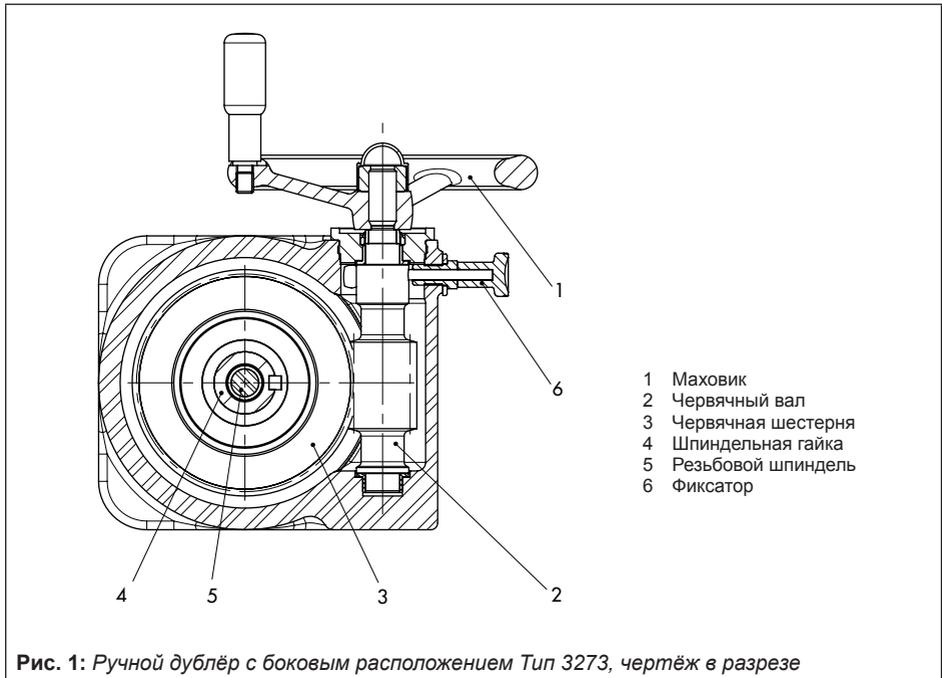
Ручной дублёр с боковым расположением Тип 3273, чертёж в разрезе
